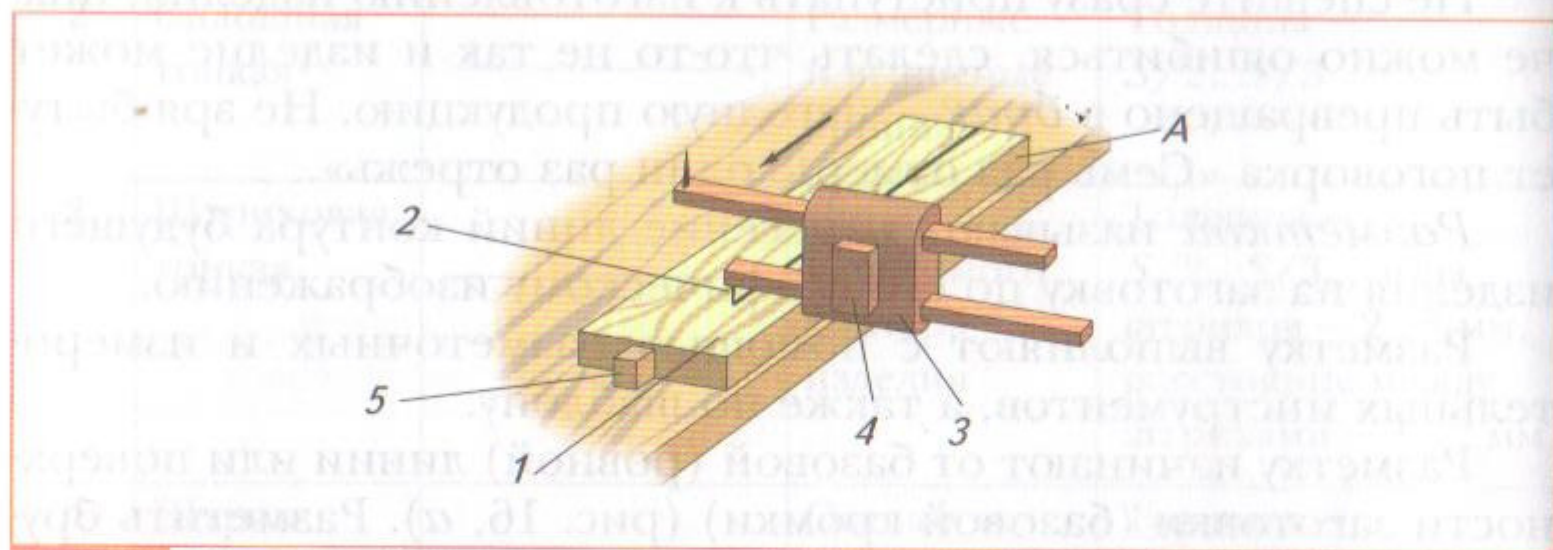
Разметка бруска рейсмусом: 1 — заготовка; 2 — остриё ножки рейсмуса; 3 — корпус рейсмуса; 4 — клин рейсмуса; 5 — упор; *A* — базовая кромка заготовки
